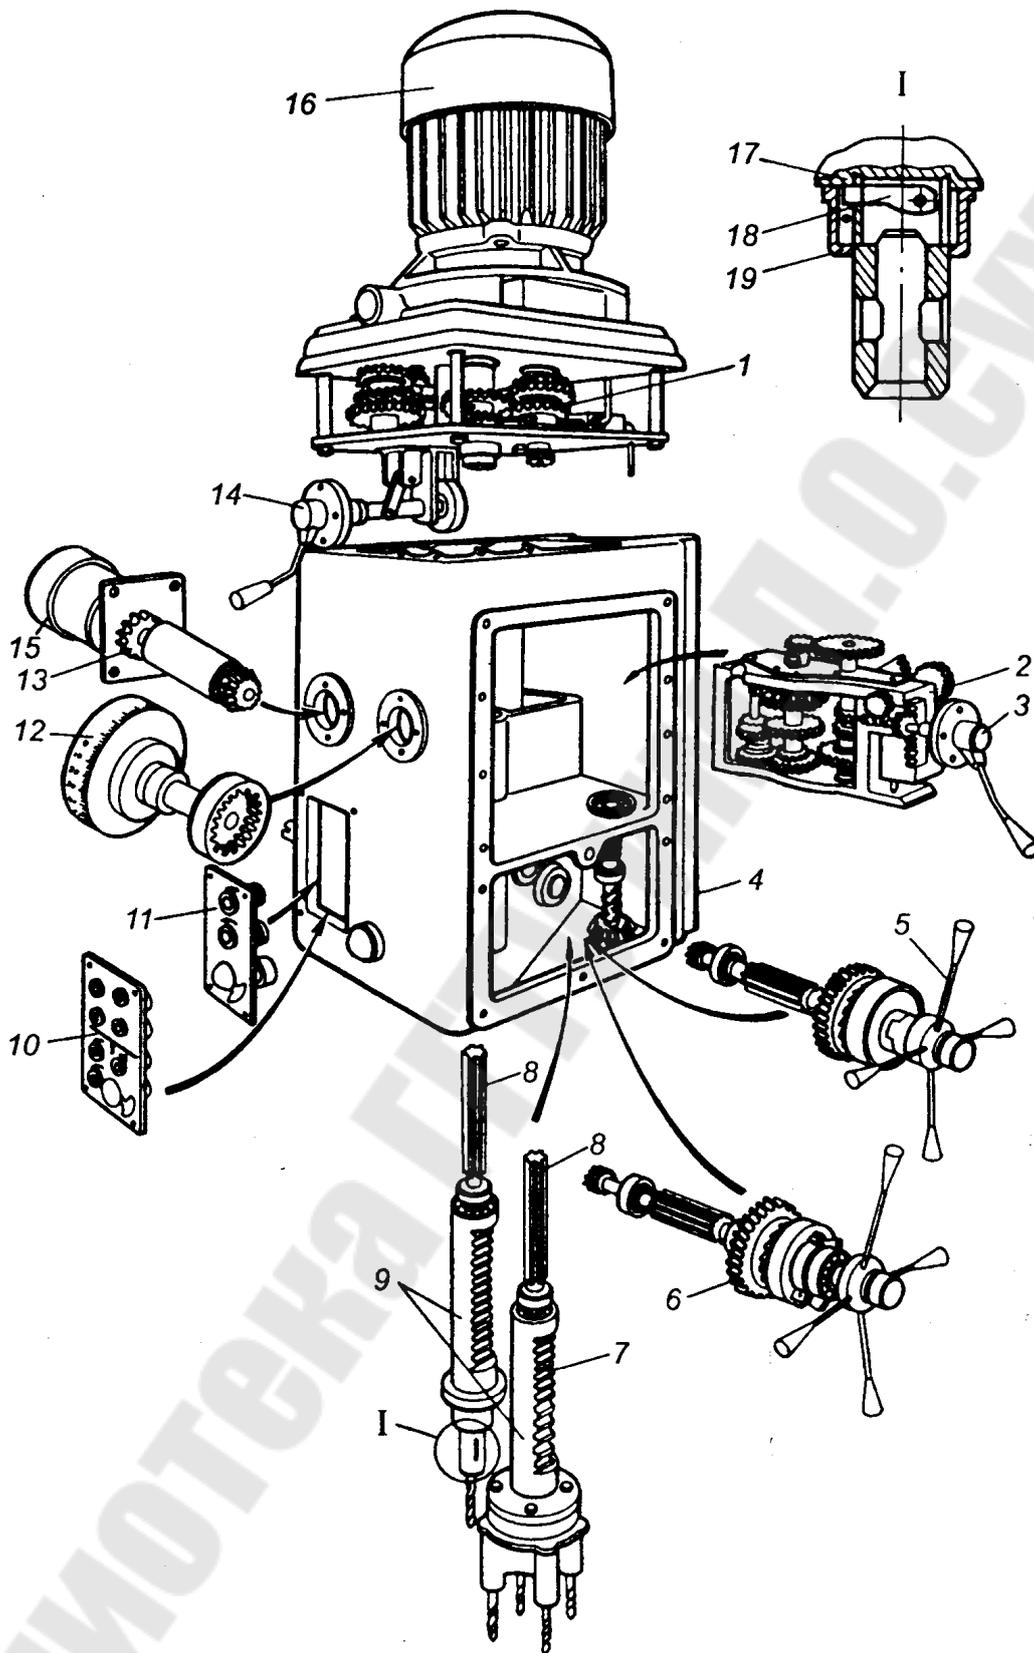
Основные узлы и детали вертикально-сверлильного станка: 1 – коробка скоростей; 2 – коробка подач; 3, 5, 14 – рукоятки управления; 4 – корпус сверлильной головки; 6, 7, 9, 13 – механизмы управления; 8 – шлицы шпинделя; 10, 11 – панели управления; 12 – лимб; 15 – электропривод ускоренного перемещения шпинделя; 16 – электродвигатель; 17 – обойма; 18 – выбивной кулачок; 19 – кожух
